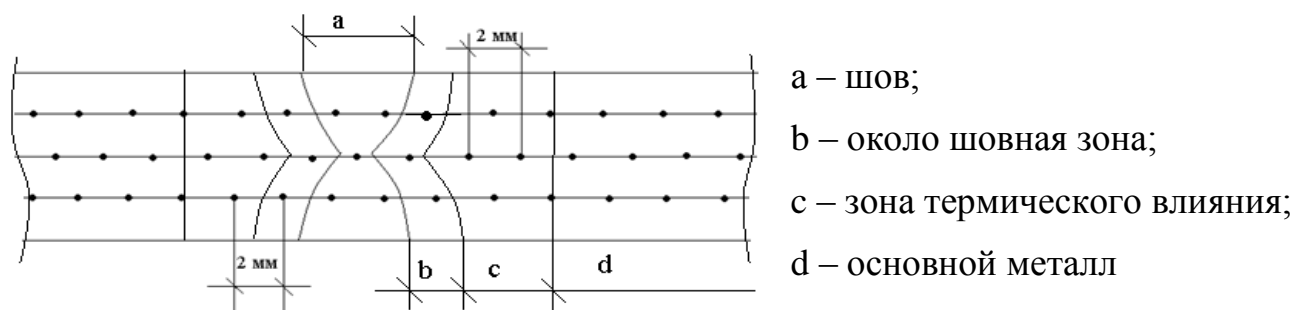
Схема проведения измерений твердости в сварном соединении
